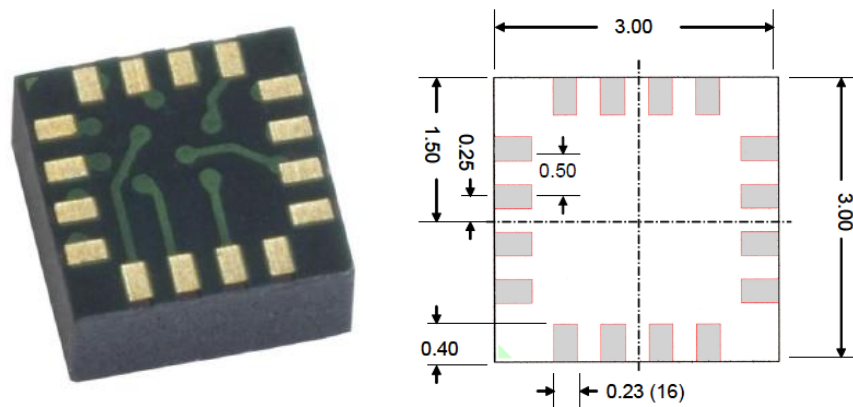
Capteur magnétique tri-axe HMC1043 de la marque Honeywell (dimensions en mm)
